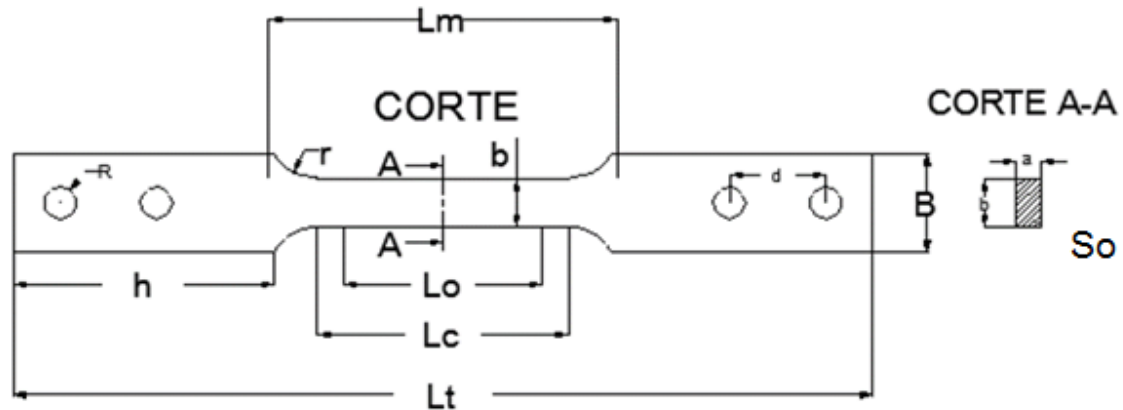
Esquema del espécimen plano de sección reducida para los Ensayos.
